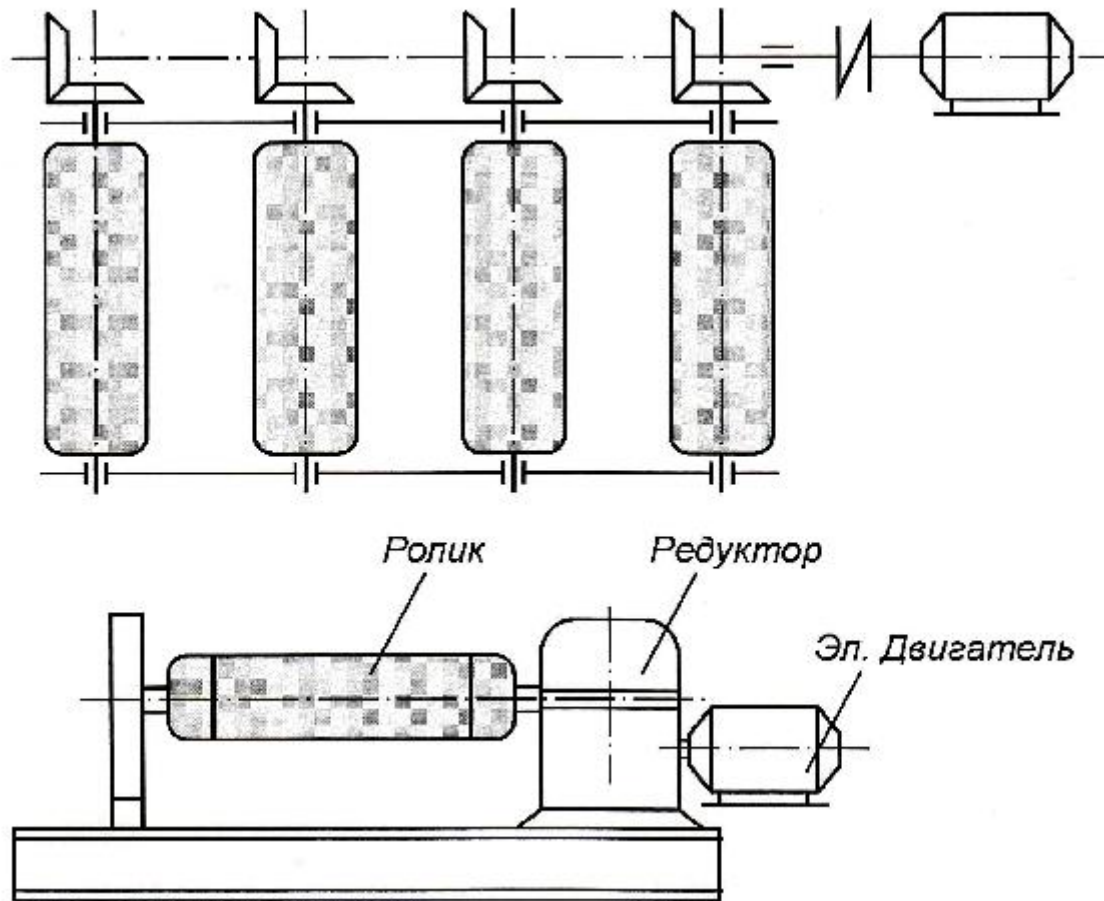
Привід від вала з конічною зубчастою передачею
